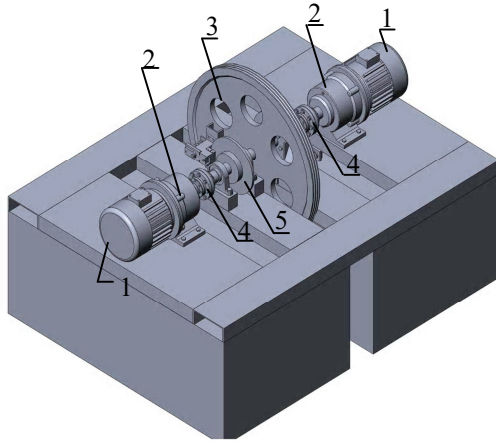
Общий вид двухдвигательного ЭП лифтового механизма подъема на базе БДПТ:
